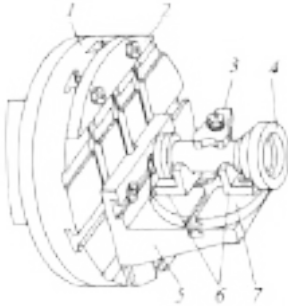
Установка заготовки складної форми на косинці: 1 — патрон; 2 — противага; 3 — притис-кна планка; 4 — заготовка; 5 — косинець; 6 — кутники; 7 — плита
